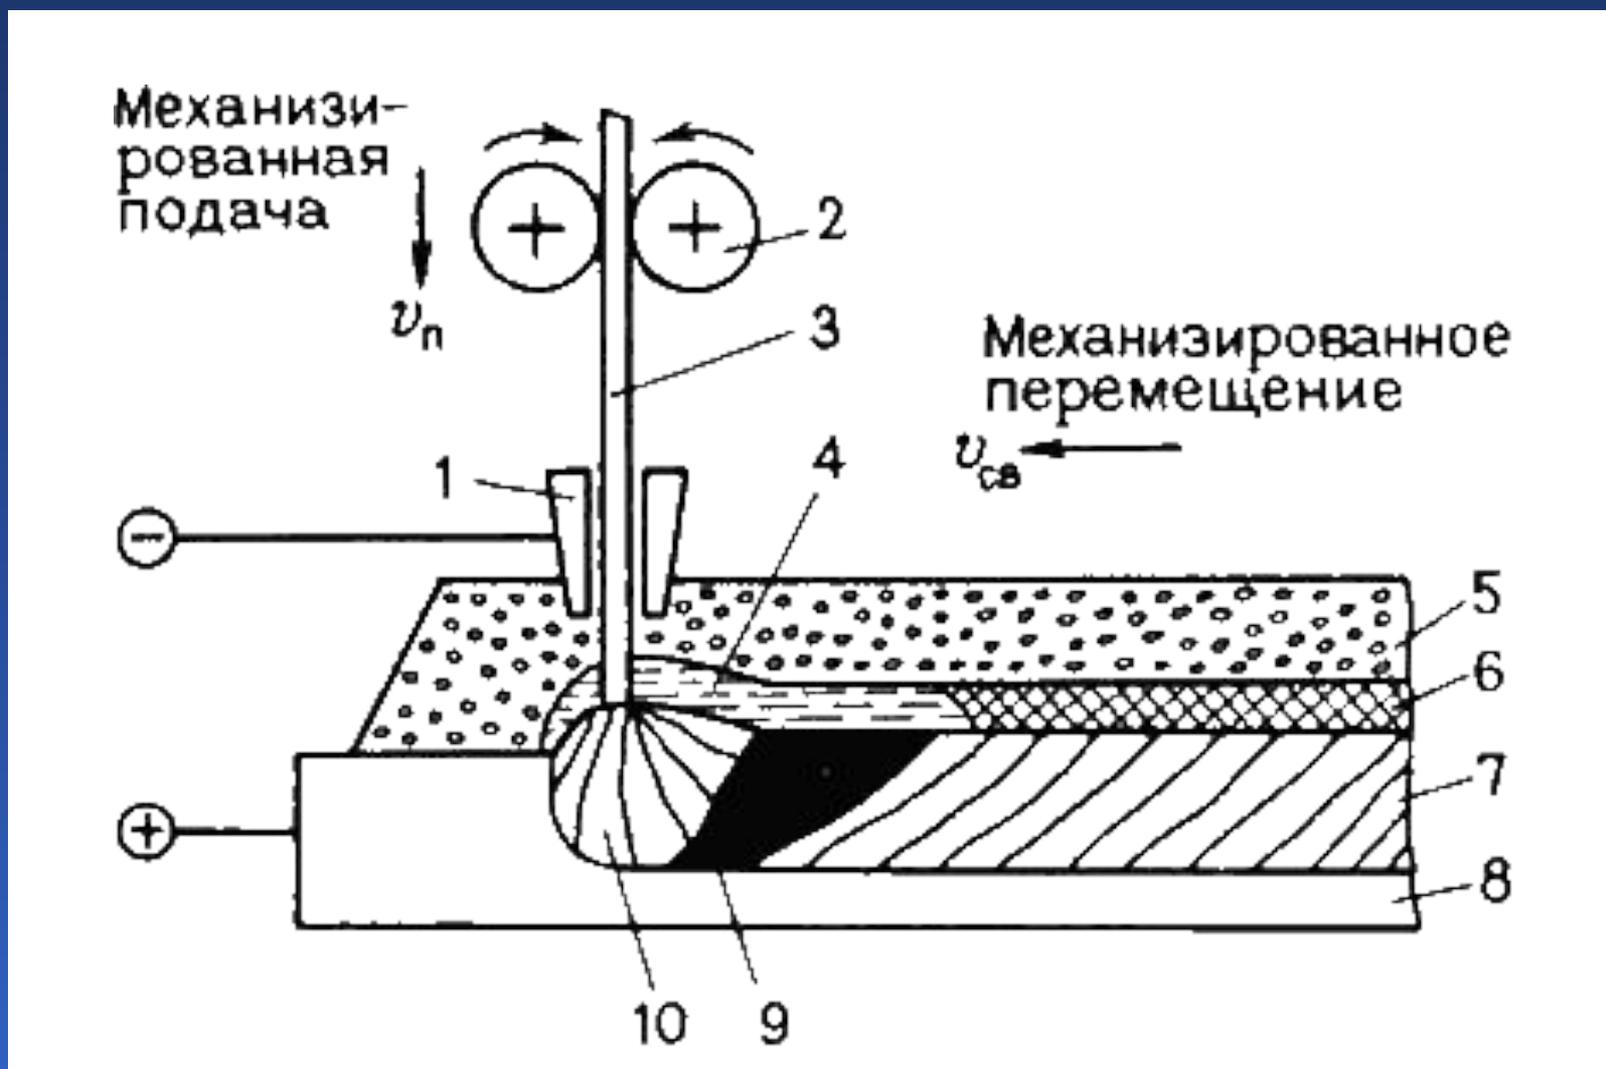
Схема процесса сварки под флюсом
